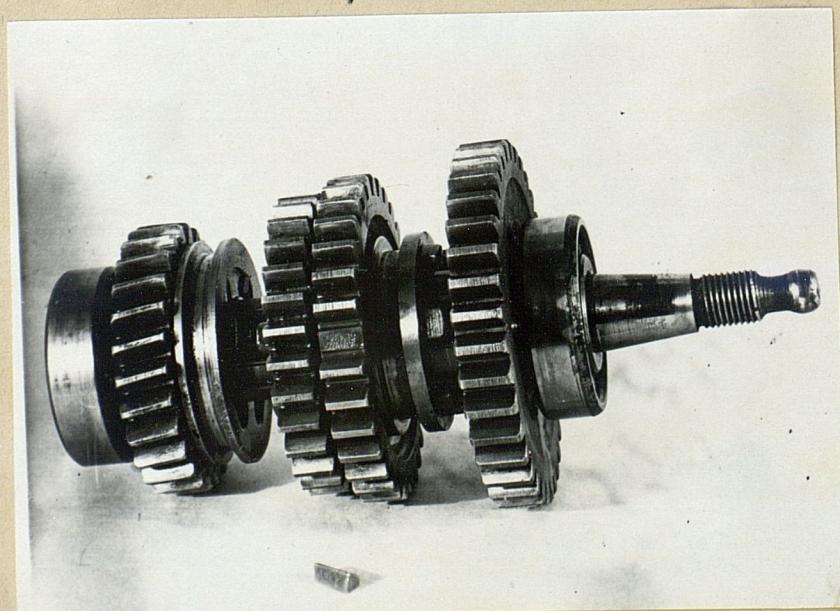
Излом зуба шестерни II-й передачи вторичного вала.
